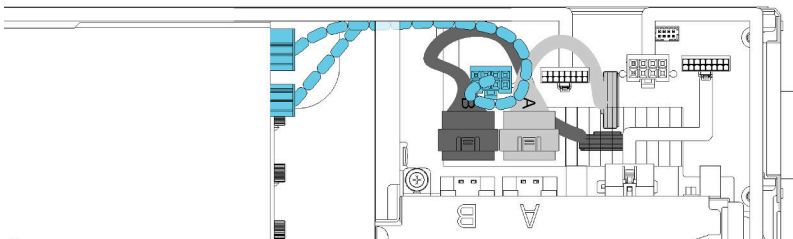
Reconexión del cable auxiliar del conjunto de expansión frontal en el nodo de expansión
